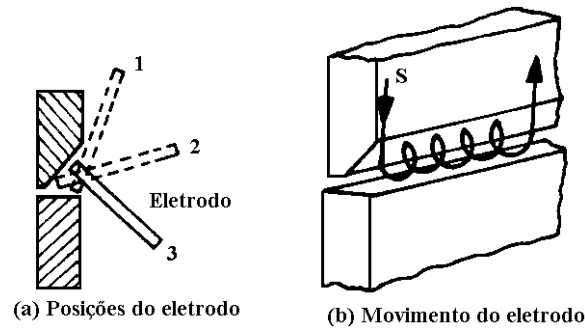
Posições de eletrodos e movimentos na soldagem horizontal.
